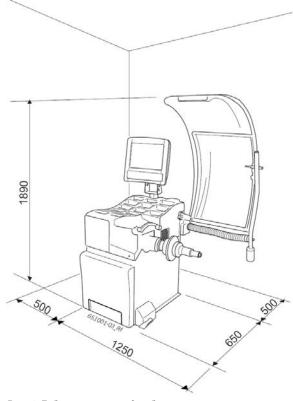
Габариты станка для балансировки колес WBE 4415.
